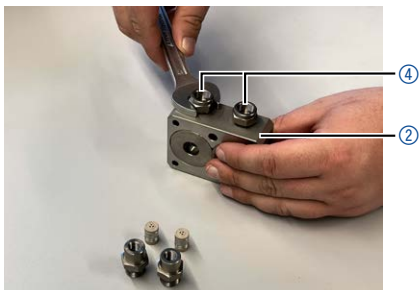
Entfernen der unteren Buchsen (Eingangverschraubungen)
